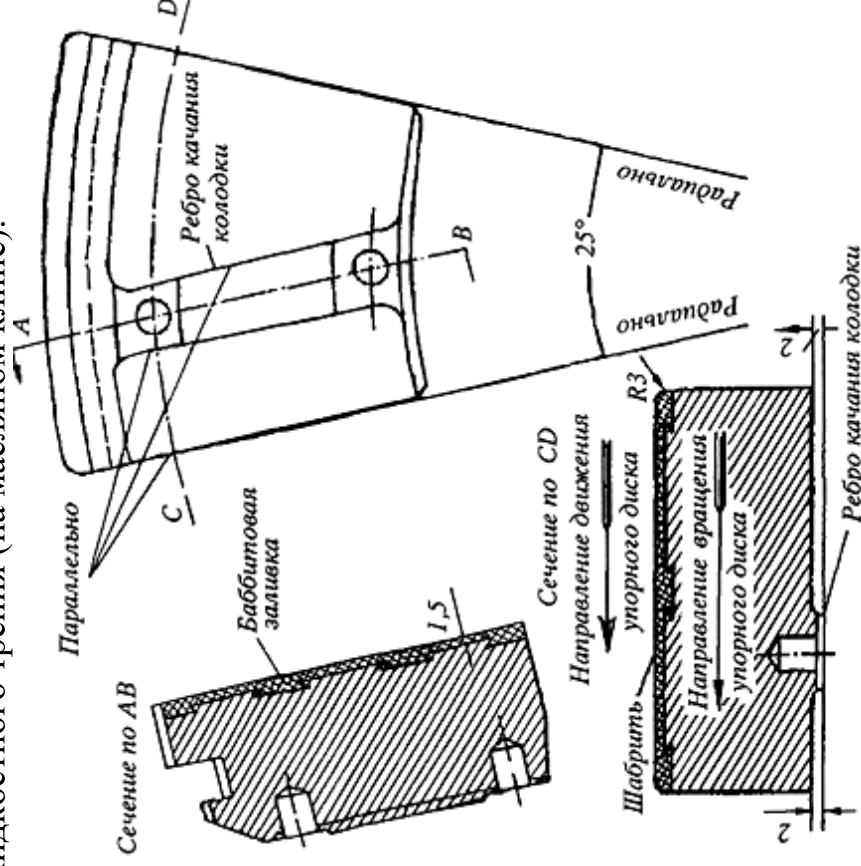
Конструкция опорного сегмента (колодки) подшипника
